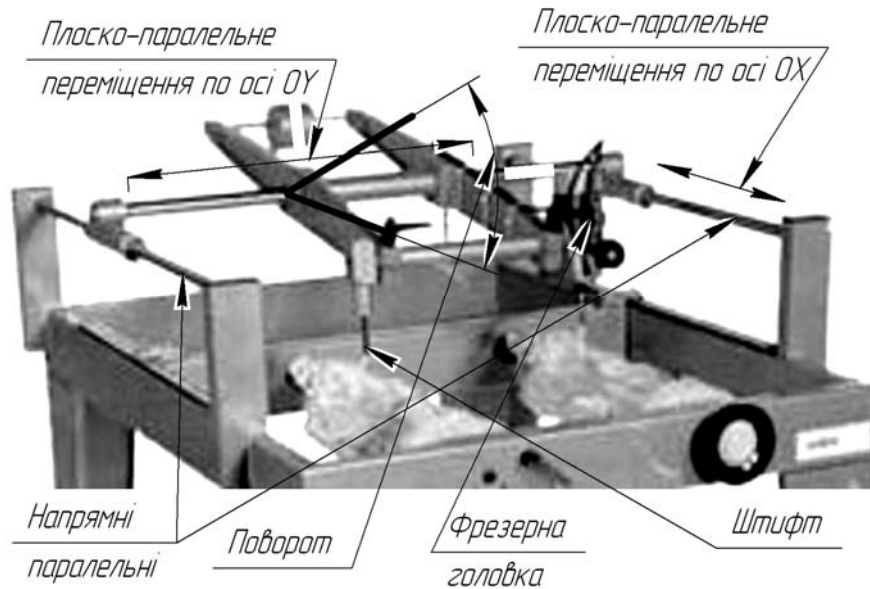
Проект фрезерного об'ємно-копіювального верстата.
